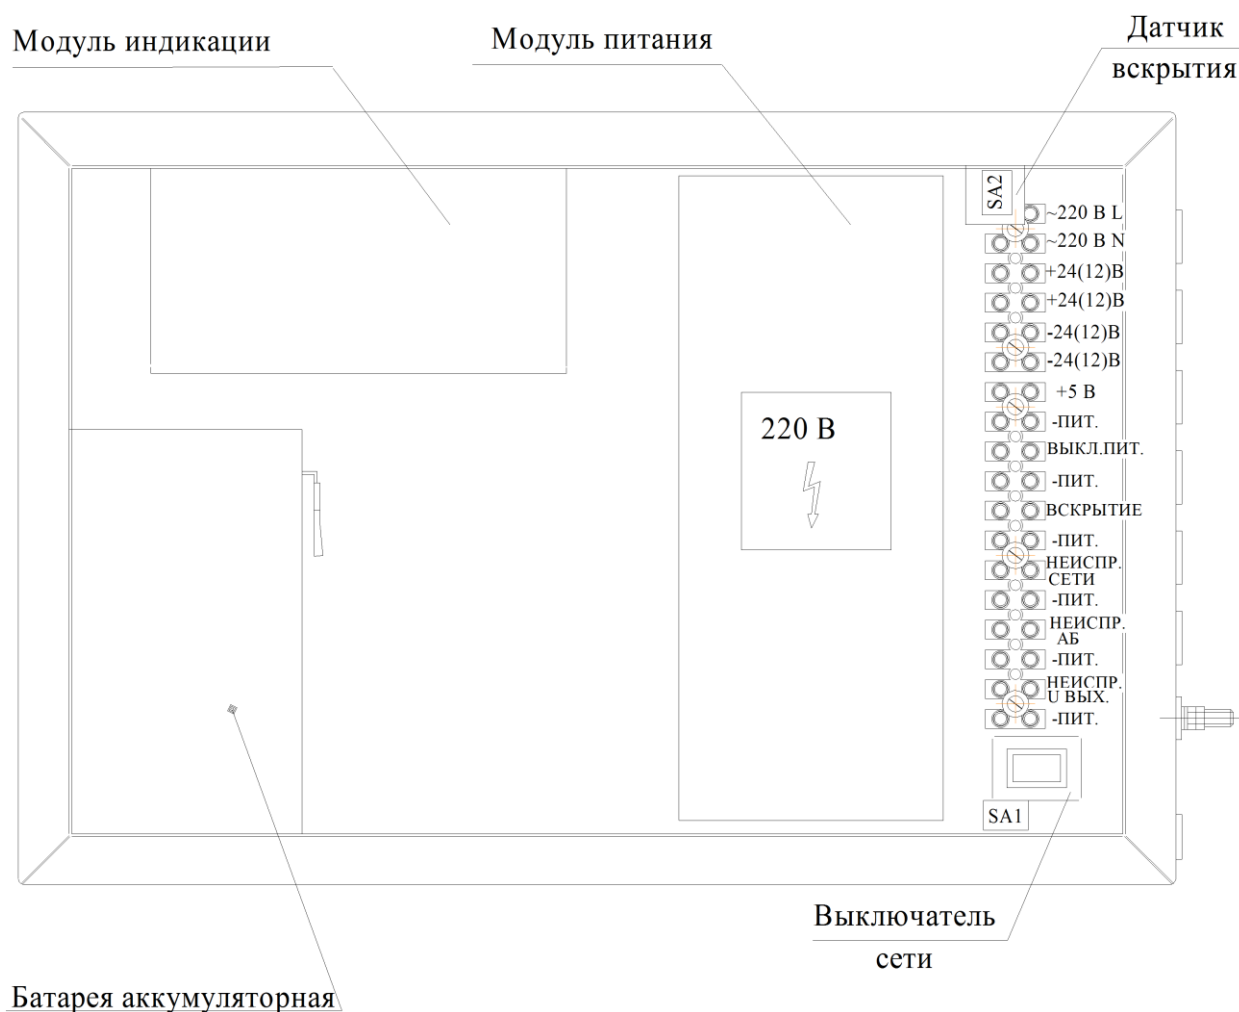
Конструктивное расположение сборочных единиц и АБ внутри корпуса ИБП «Крон-12/2»
